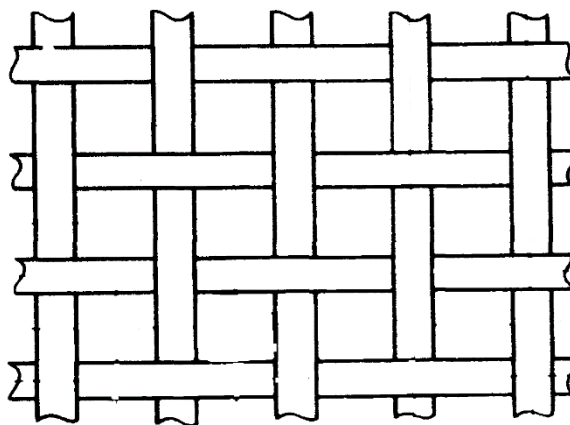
Типова конструкція металевої сітки з квадратною лункою
